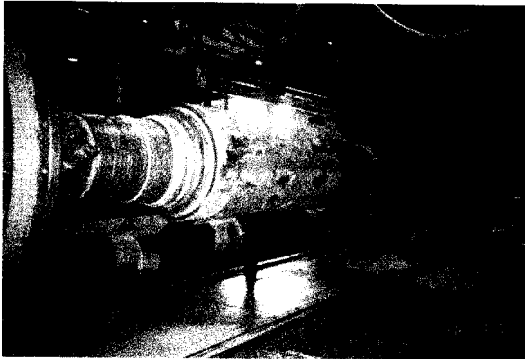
Vista da operação de soldagem com arco submerso para recuperação do mancal de um rolo de laminação de ferro fundido
